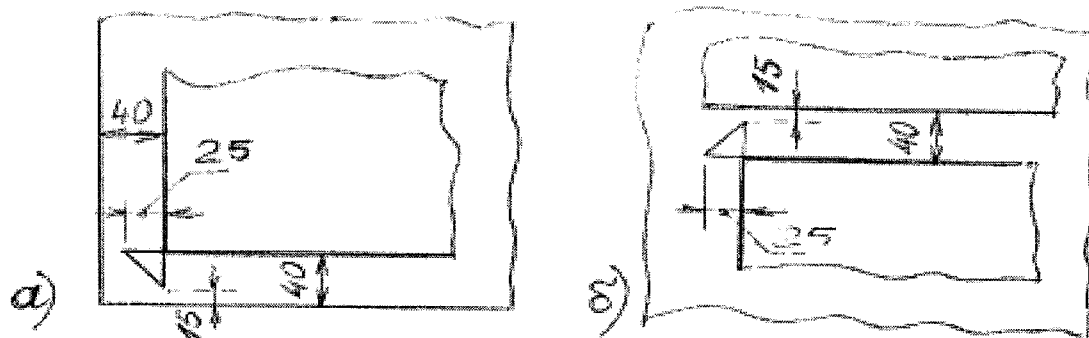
а) ОБРАЗЕЦ, расположения детали относительно края листа;
